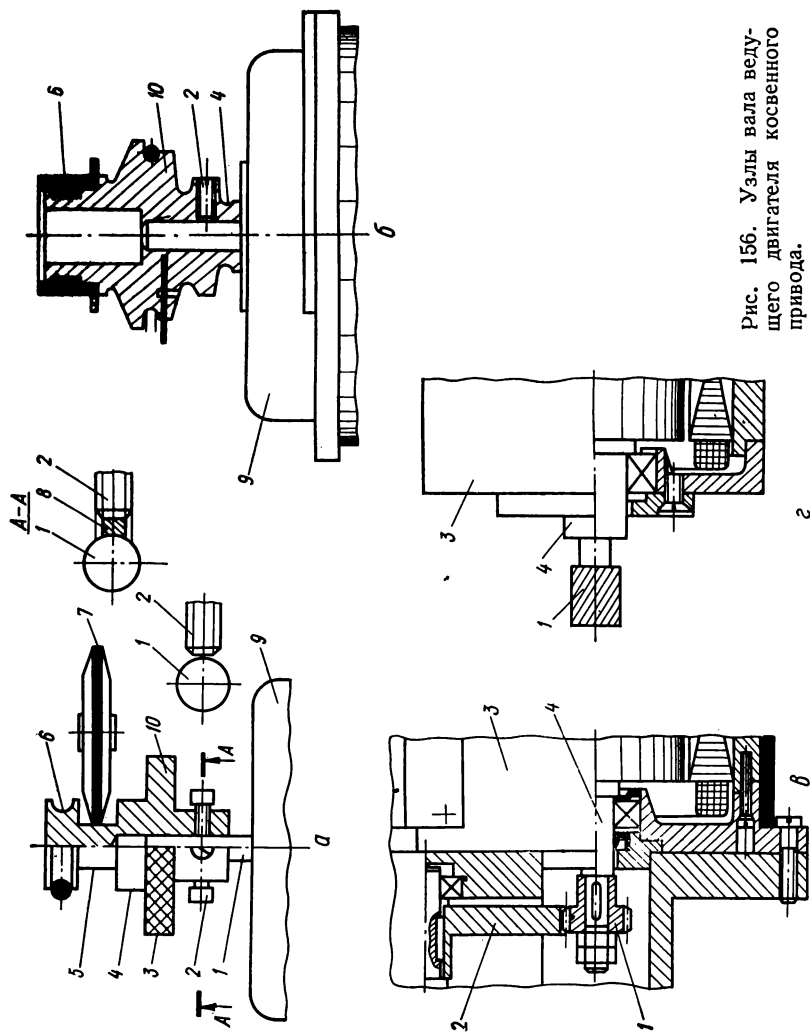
Узлы вала ведущего двигателя косвенного привода.
